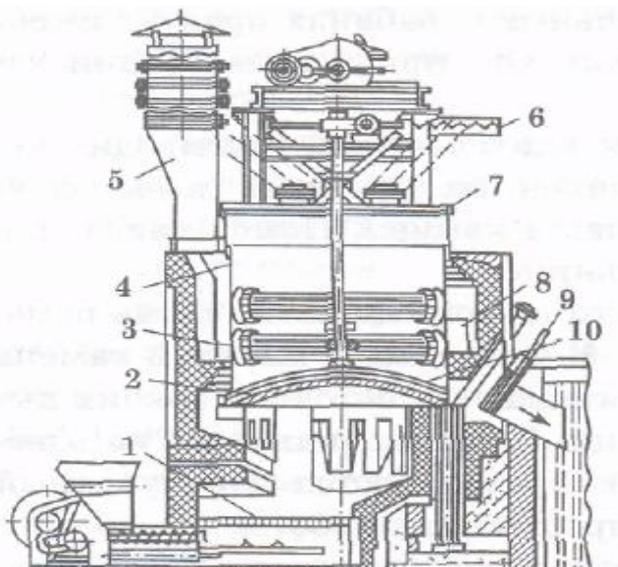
Гипсоварочный котел: 1 - топка; 2 - сферическое днище; 3 - жаровые трубы; 4 - стальной барабан; 5 - дымовая труба; 6 - винтовой конвейер; 7- крышка; 8 - кольцевые каналы; 9 - шибер; 10 - мешалка
